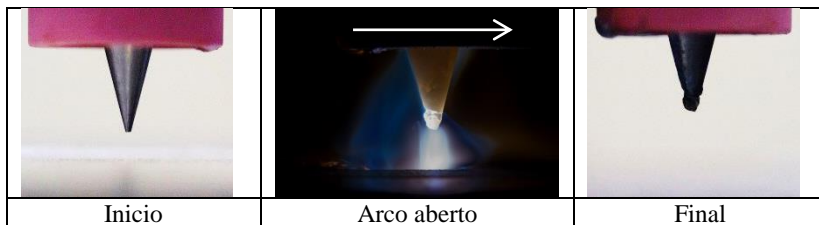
Desgaste do eletrodo para uma velocidade de soldagem de 50 cm/min com argônio como gás de proteção usando a técnica *Keyhole*.
